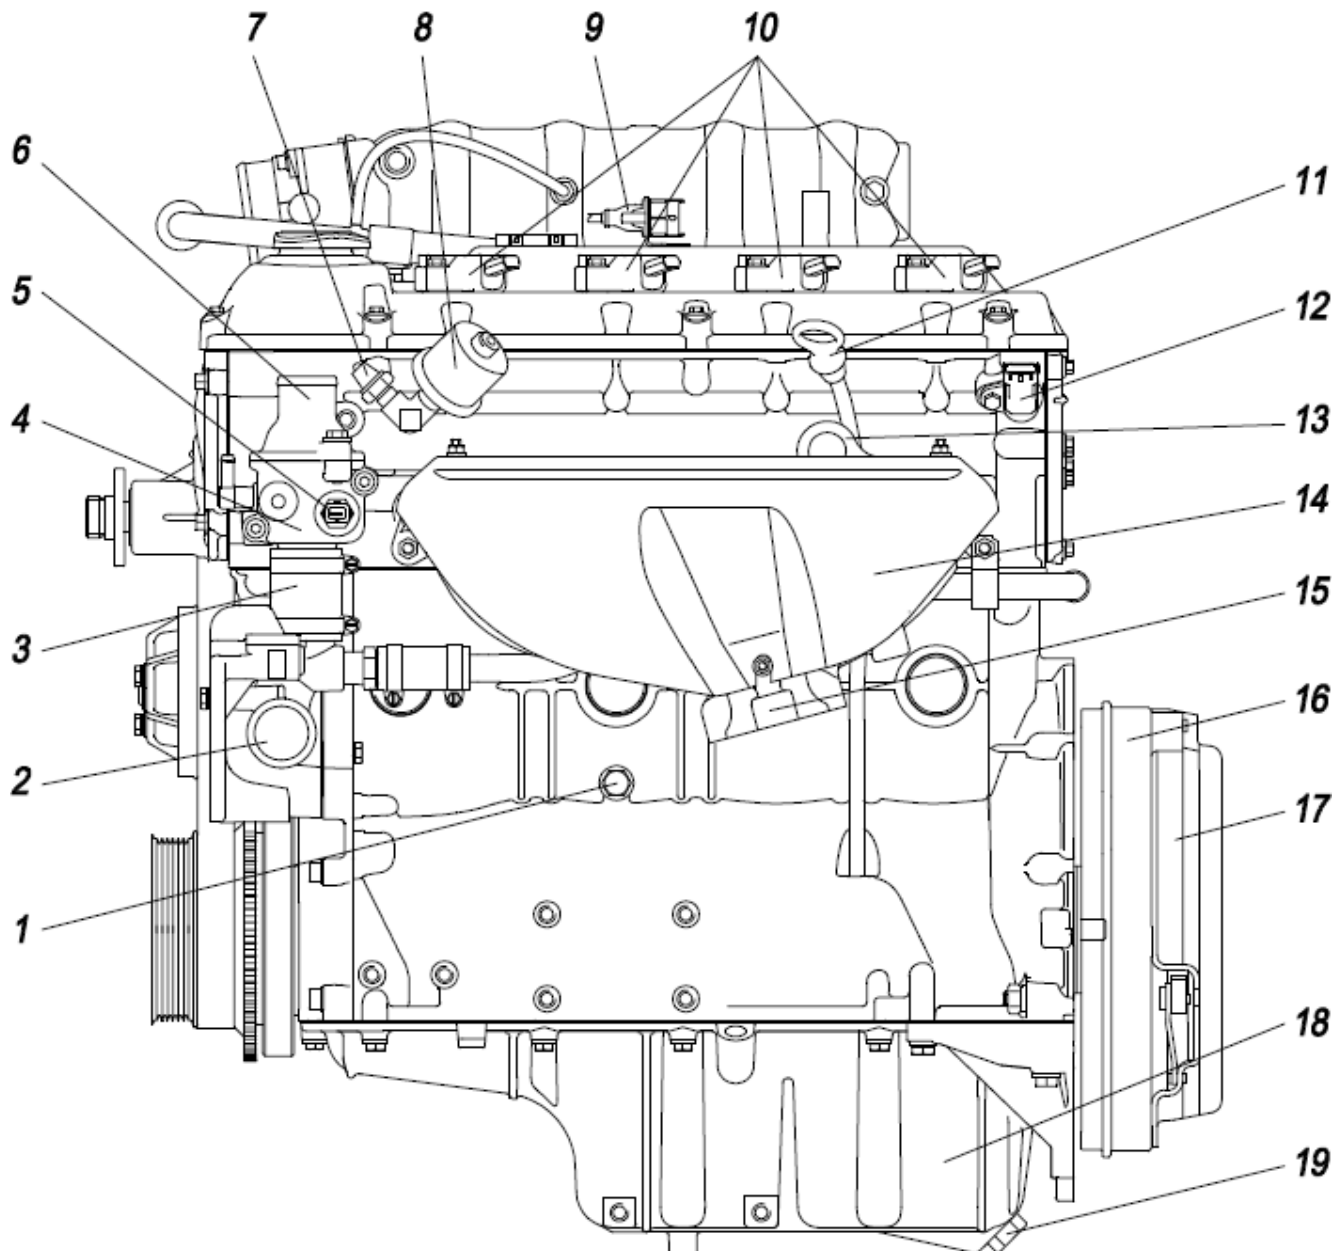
Вид справа двигателя ЗМЗ-40904.10:
